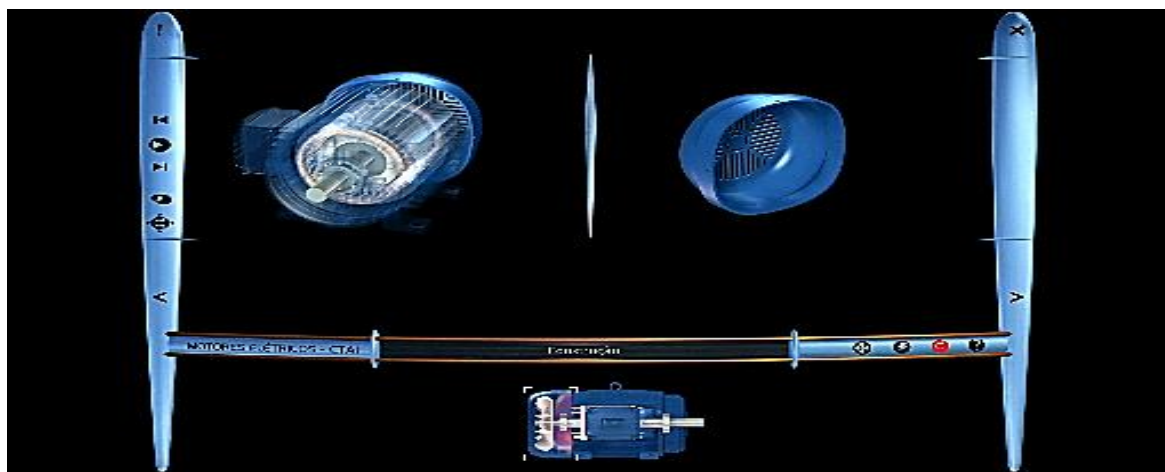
Partes de un motor trifásico (piezas dentro de la carcasa).
